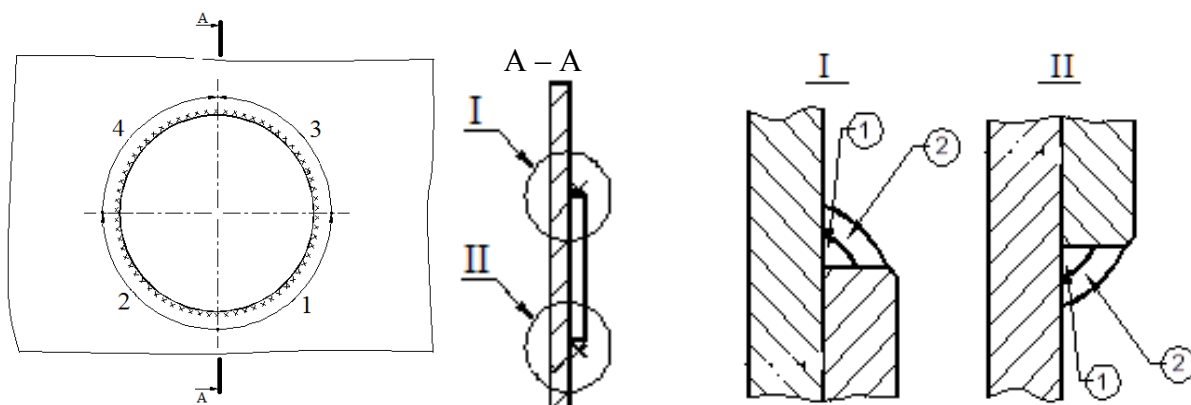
Последовательность и схема сварки ветрового кольца
